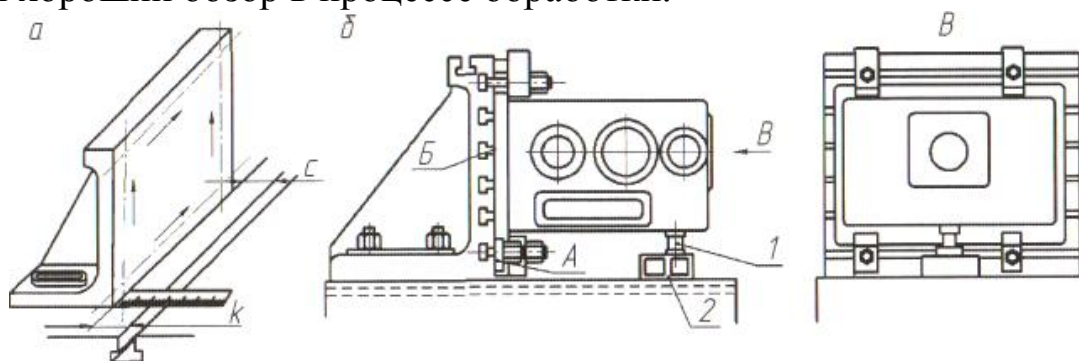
Схема выверки угольника (а) и установка корпуса на угольнике (б): 1 – опора; 2 – плоская подкладка или брусок; А – крепление заготовки к угольнику; Б – Т-образные пазы угольника
